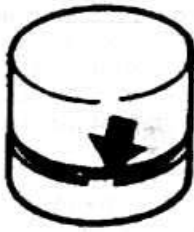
Толкатели клапанов необходимо держать вертикально, смазочная канавка показана стрелкой вниз — двигателя с двумя распредвалами
